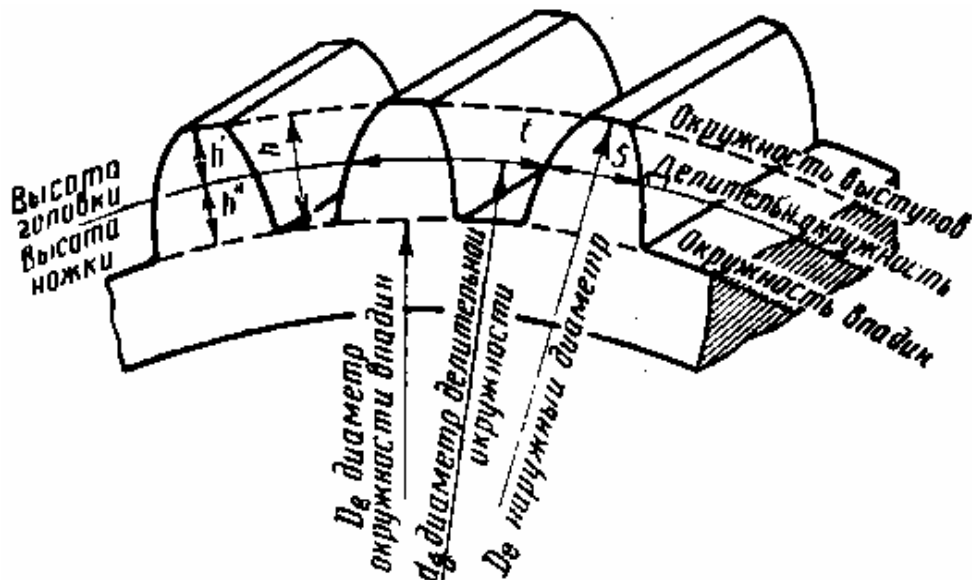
Элементы цилиндрического зубчатого колеса
